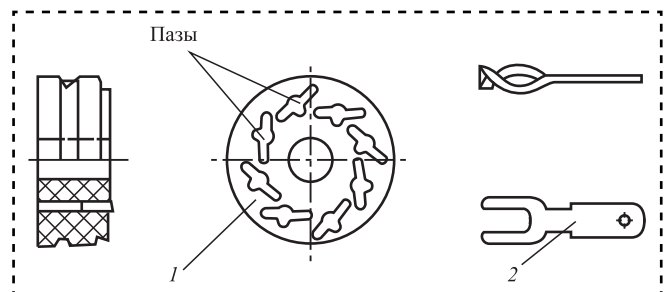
Схема сборки корпуса с контактным пакетом ЭС и кантования его в позицию завальцовки:
